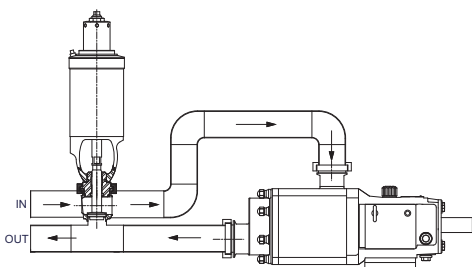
WR61C Luftsteigventil mit einstellbarem Federstellglied
